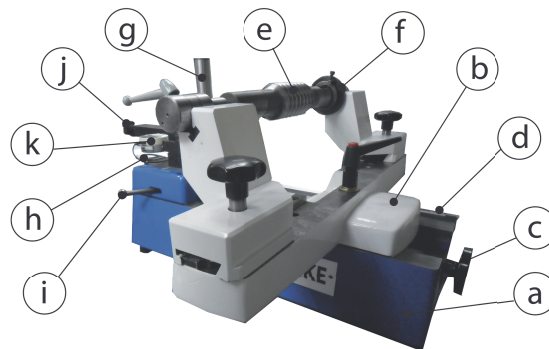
Máquina de ensayos de rodadura a dos flancos para sinfín corona
